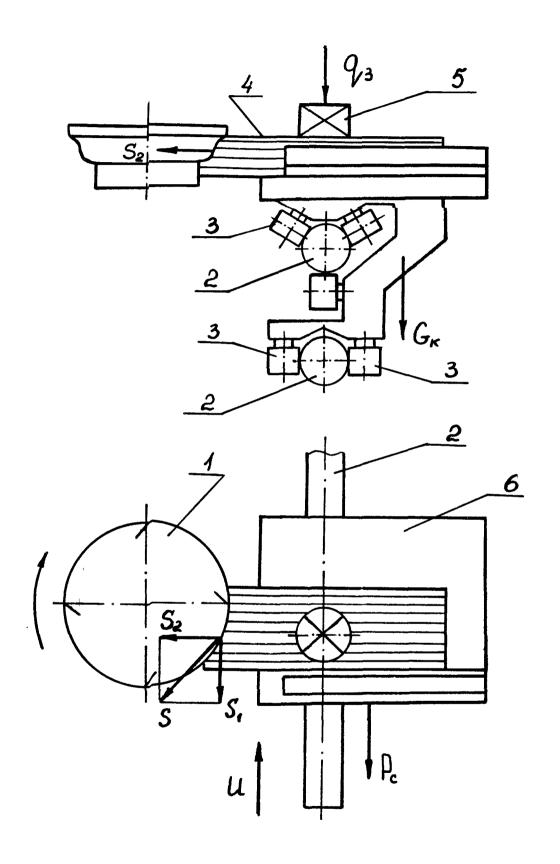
Функциональная схема фрезерного станка с шипорезной кареткой: 1 - фреза; 2 - направляющая; 3 - опора качения; 4 - заготовка; 5 - зажим; 6 - каретка
